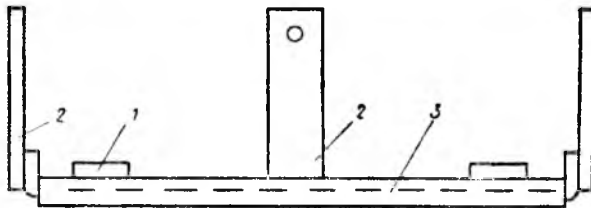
Платформа батареи культиватора ДЛКН-6/8 (вид спереди):
